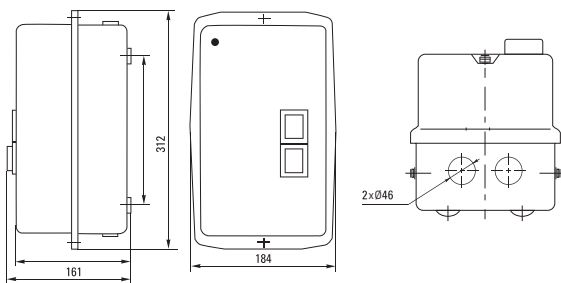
Габаритные размеры для ПМЛ 40-95А
